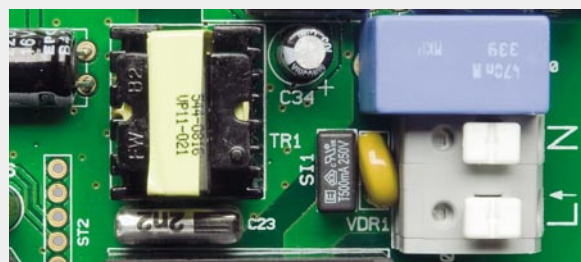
Die bessere Sicherungslösung – eine Kleinstsicherung (SI 1) auf der Platine
